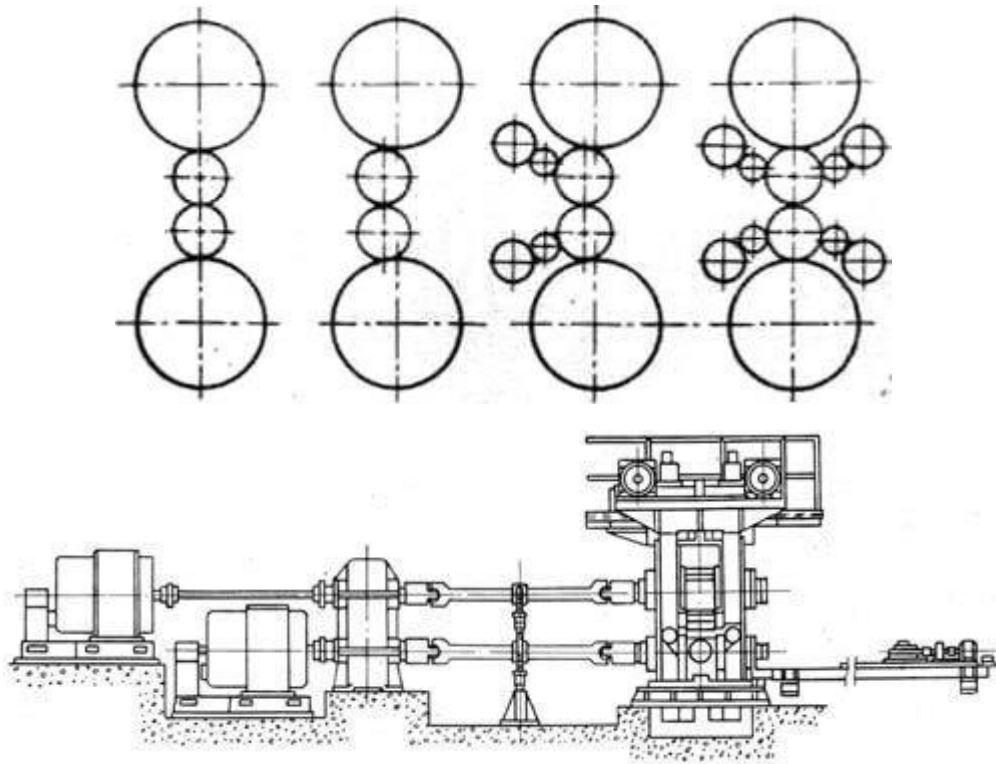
Чотирьохвалковий стан з приводом опорних валків
